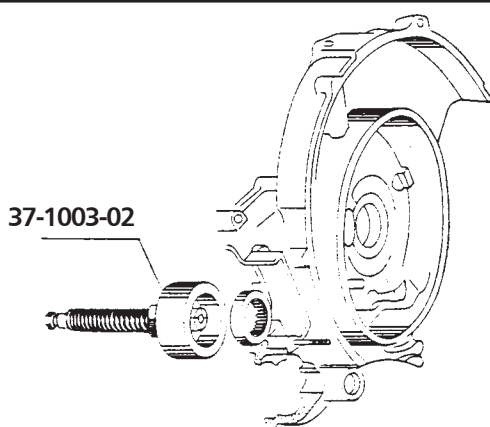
Remoción del cojinete de rodillos del eje principal.
